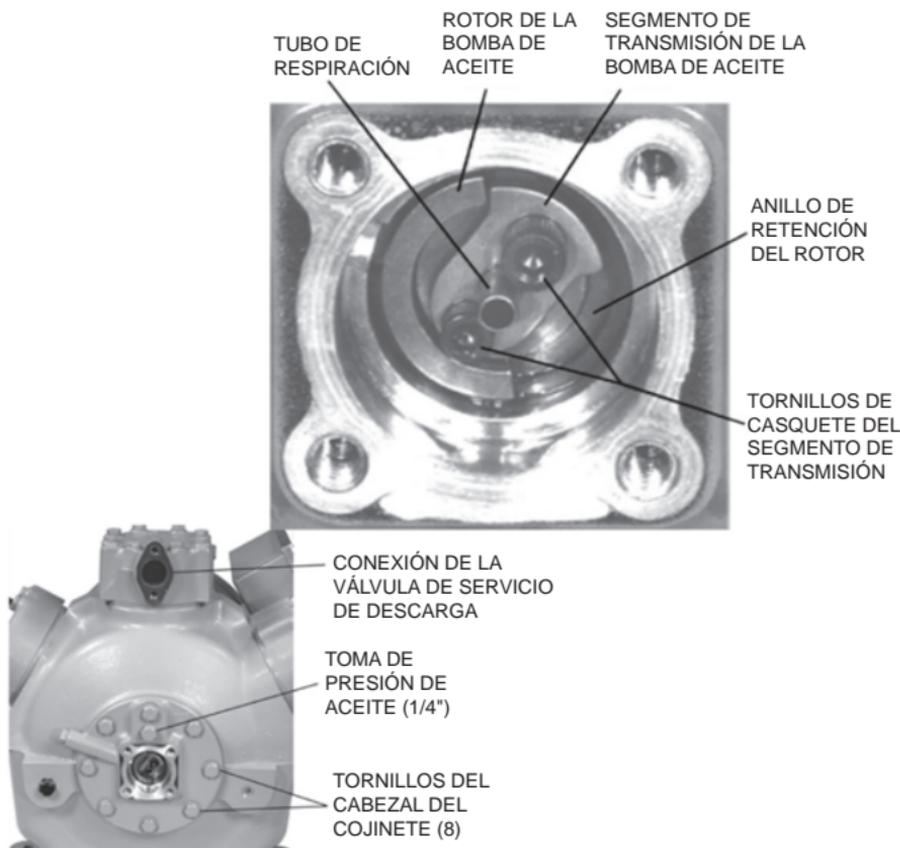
Extracción del cabezal del cojinete del extremo de la bomba (compresor 06D)
